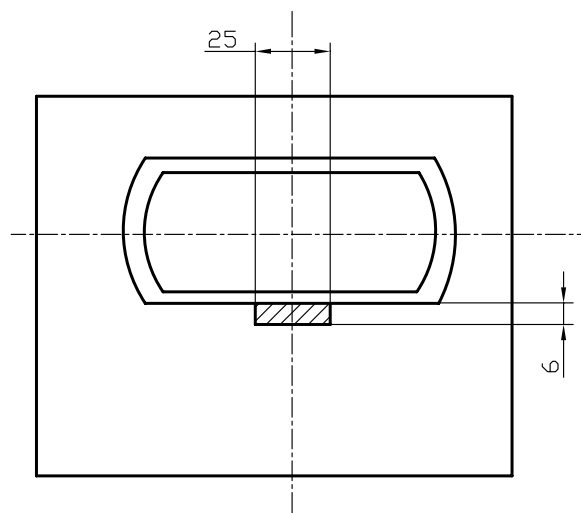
(2) 底角件偏置时的承载面示意图 (单位: mm)
